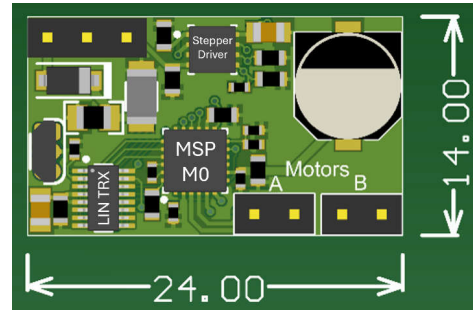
HVAC 阀门用紧凑型智能执行器 PCB
